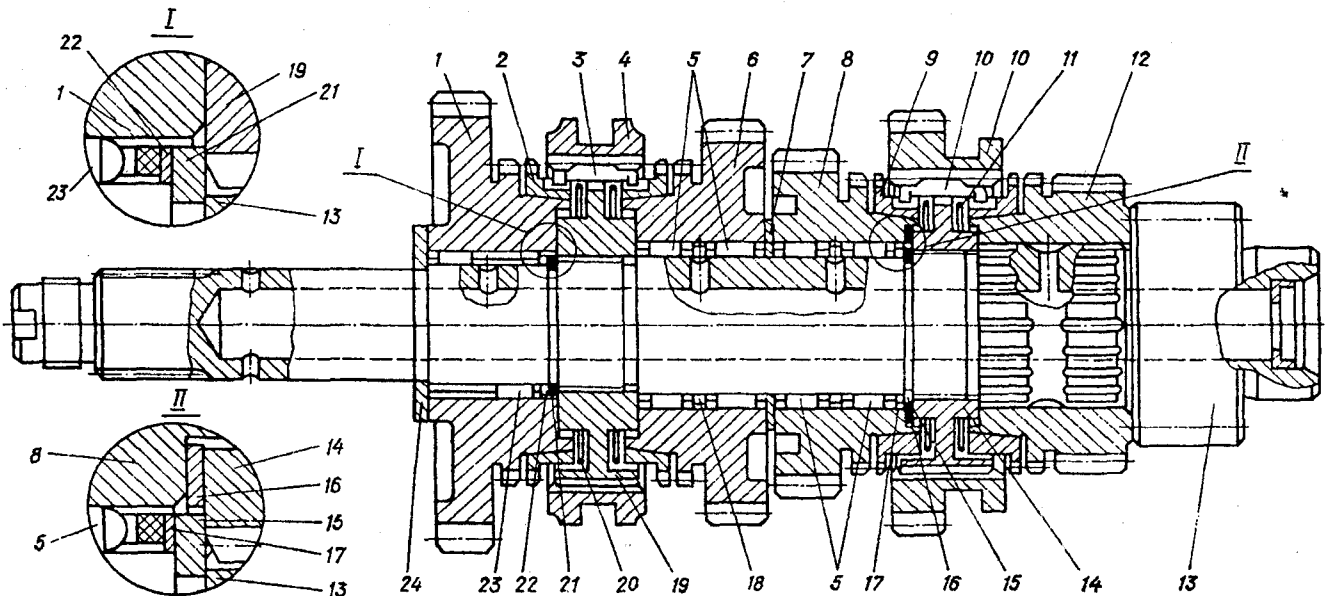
Ведомый вал в сборе (ведущая шестерня-вал главной передачи): 1, 6, 8 и 12 – шестерни ведомые первой, второй, третьей и четвертой передач; 2 и 9 – кольца, блокирующие синхронизаторы первой-второй и третьей-четвертой передач; 3 – сухарь синхронизатора; 4 – муфта выключения синхронизатора первой и второй передач; 5 – подшипники ведомых шестерен второй и третьей передач; 7, 16 – шайбы упорные; 10 – шестерня ведомая заднего хода; 11 и 20 – пружины синхронизатора третьей-четвертой и первой-второй передач; 13 – шестерня ведущая главной передачи; 14 и 19 – ступицы муфт переключения третьей-четвертой и первой-второй передач; 15, 21 – кольца стопорные; 17, 22 – кольца; 18 – проставочное кольцо; 23 – подшипник ведомой шестерни первой передачи; 24 – шайба упорная
